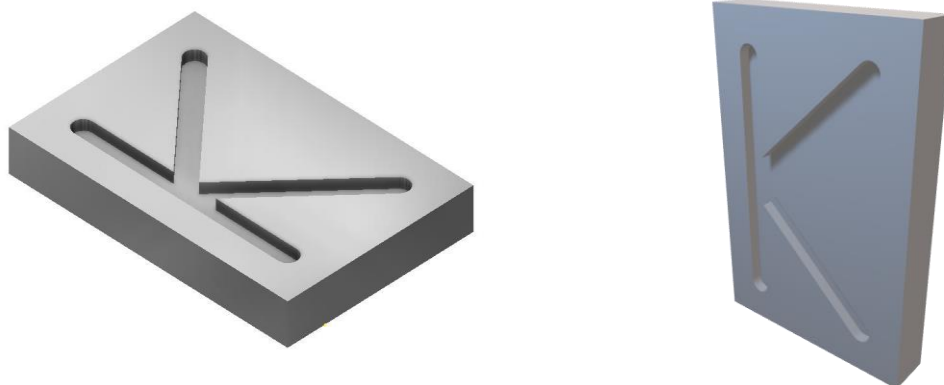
Τρισδιάστατη απεικόνιση αποστολής 2
